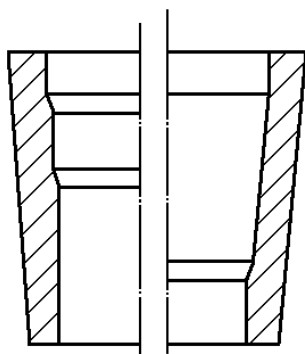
Типовой эскиз внутренней поверхности деталей, формируемой при деформировании
